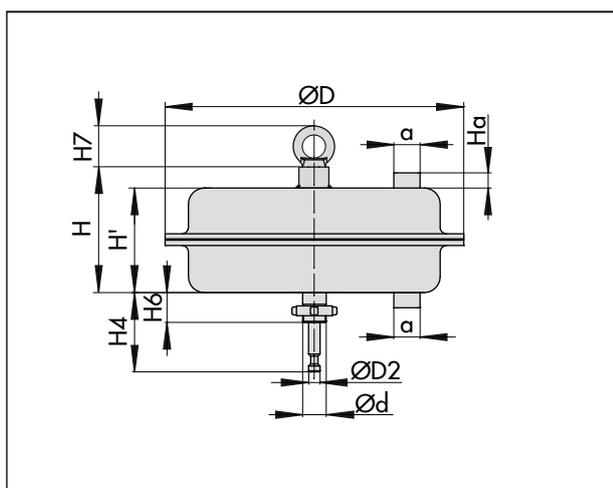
Type 3271 avec surface de 750v2 cm²
